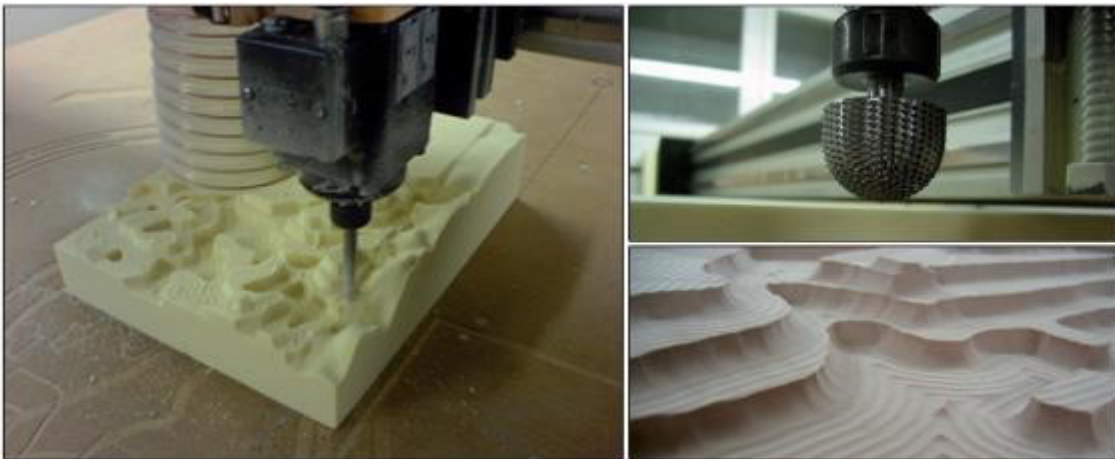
Testfräsung mit einer CNC-Maschine des Raplab der ETH Zürich (links), Kugelfräskopf einer CNC-Maschine (rechts oben), Geländereief nach der ersten Bearbeitungsphase [RÄB-08: 192]
